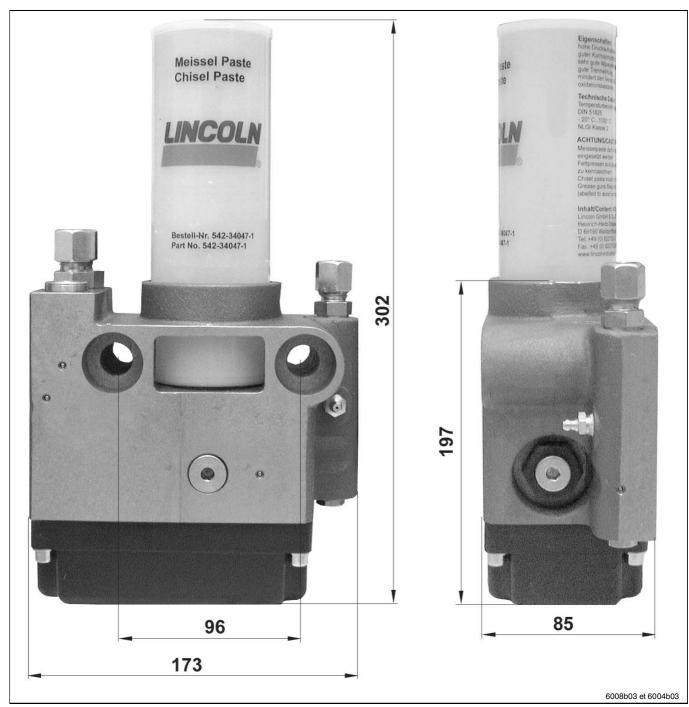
Dimensions de la pompe de lubrification hydraulique HTL 101 (cotes en mm)
